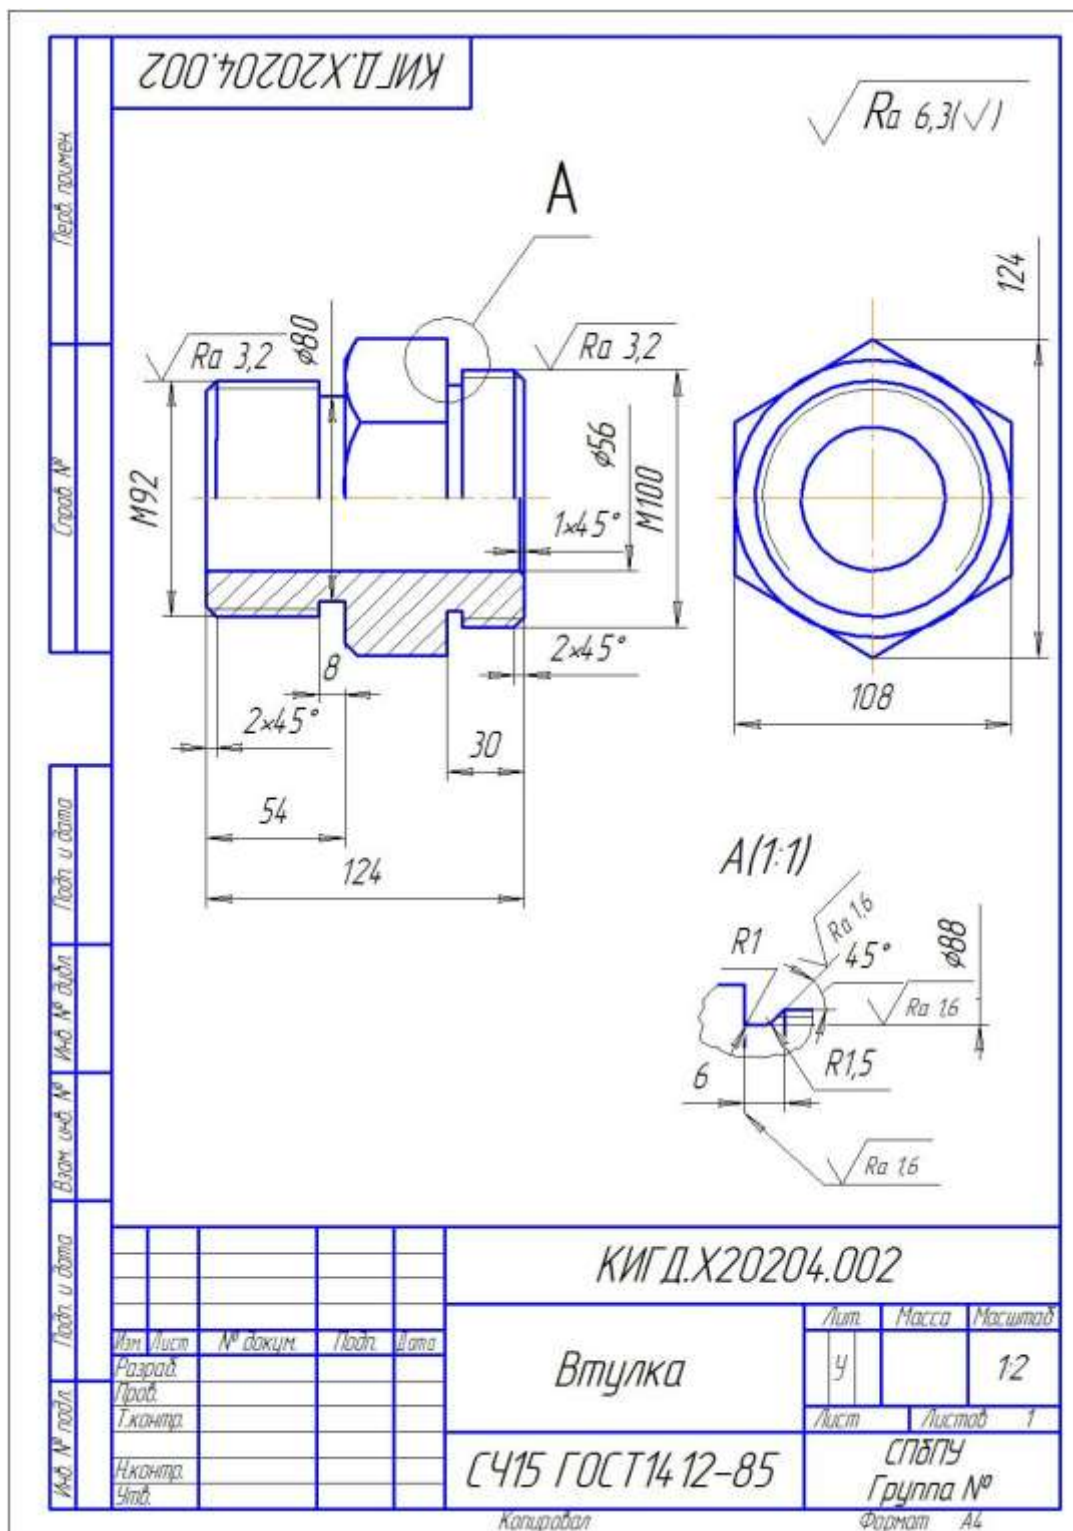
Пример выполнения рабочего чертежа детали №2- Втулка
